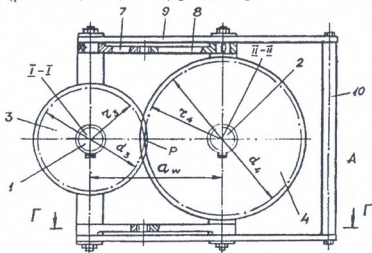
Одноступенчатый эллипсоидный зубчатый вариатор
